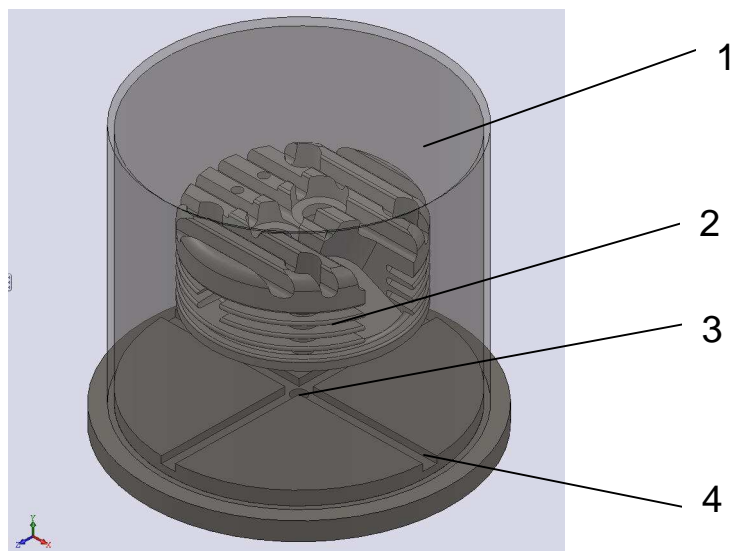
Камера термоимпульсной машины с обрабатываемой деталью: 1 – корпус камеры; 2 – обрабатываемая деталь; 3 – отверстие для подачи смеси; 4 – паз
